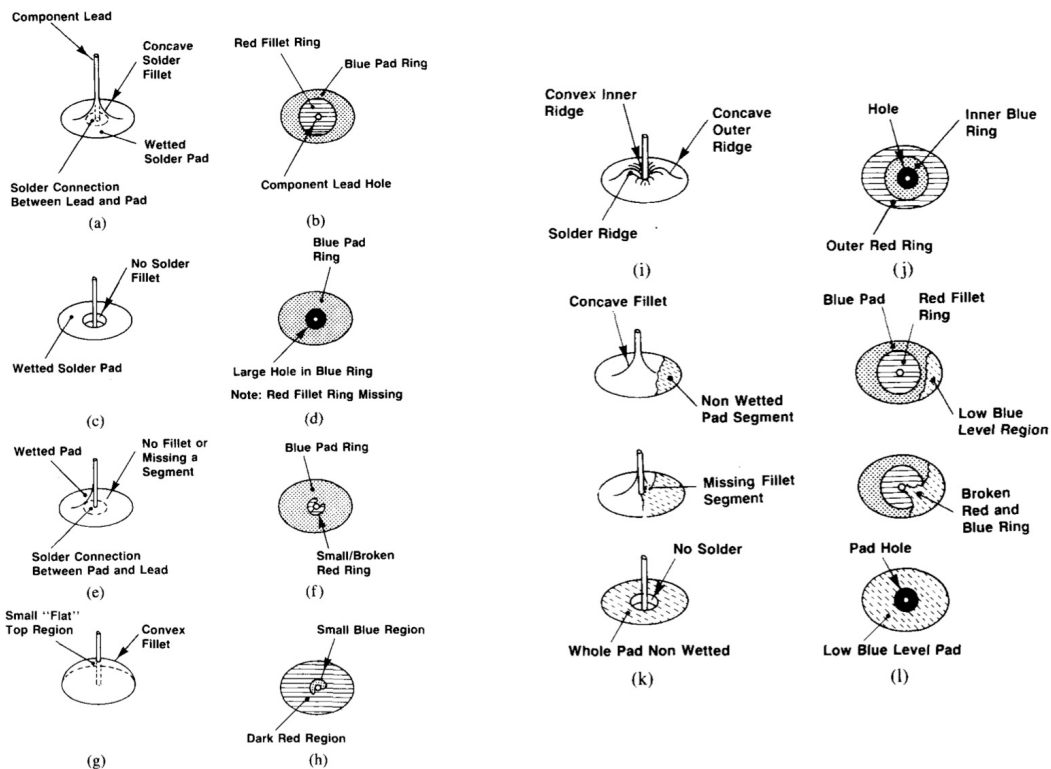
Difetti delle saldature e relative immagini “Tiered-Color Illumination”: (a) good solder joint, (b) good solder joint color contours, (c) no solder, (d) color contours for no solder, (e) insufficient solder, (f) color contours for insufficient solder, (g) excess solder, (h) color contours for excess solder, (i) poorly wetted lead, (j) contours of poorly wetted lead, (k) poorly wetted pad, (l) contours of poorly wetted pad.
